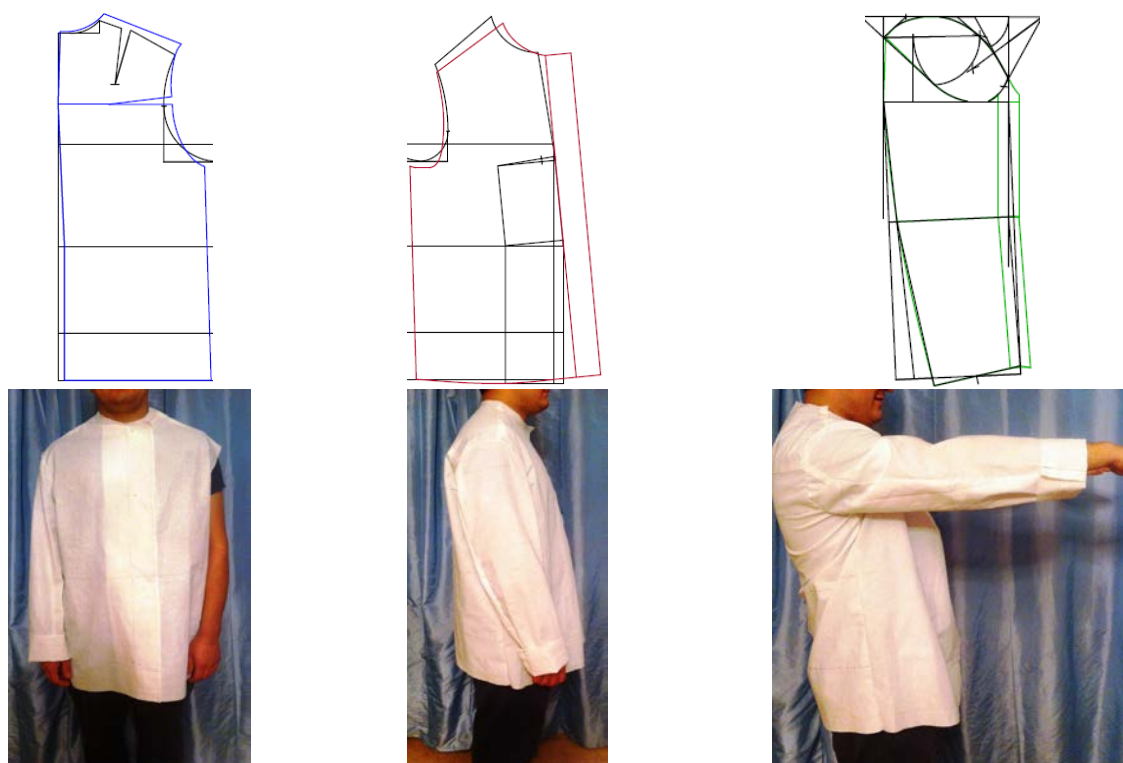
Разработка конструкции и изготовление макета куртки сварщика
